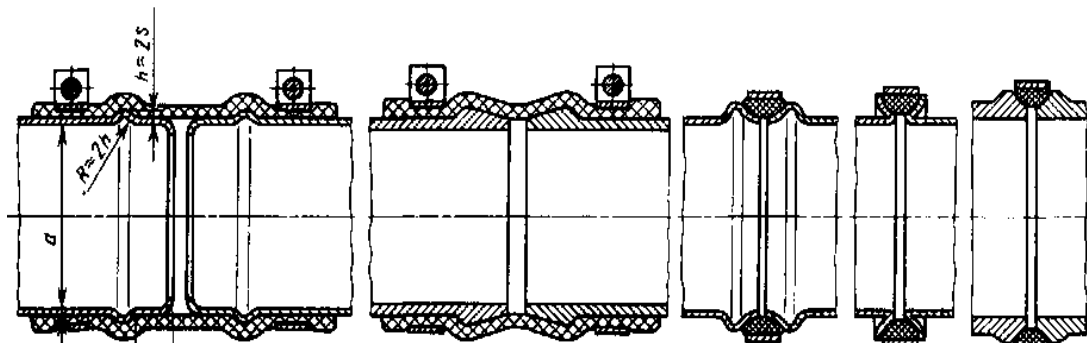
Соединение трубопроводов мягкими рукавами
